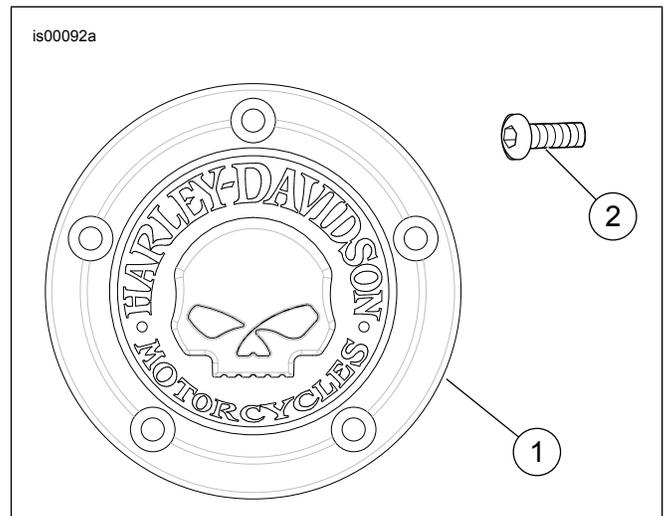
Piezas de servicio: Kit de cubierta para cronómetro
